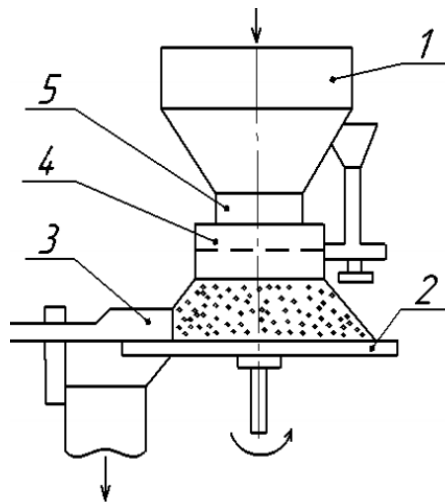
Тарілчастий дозатор: 1 - бункер; 2 - тарілка; 3 - скребок; 4 і 5 - рухливий і нерухомий патрубки
